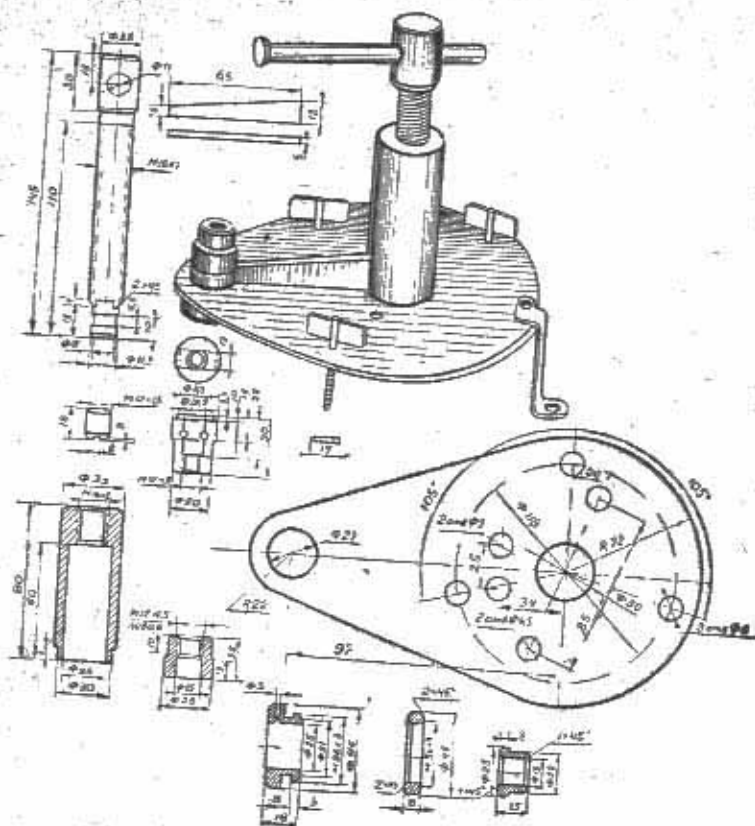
Приспособление для распрессовки и запрессовки коленчатого вала и разъединения половин картера.
